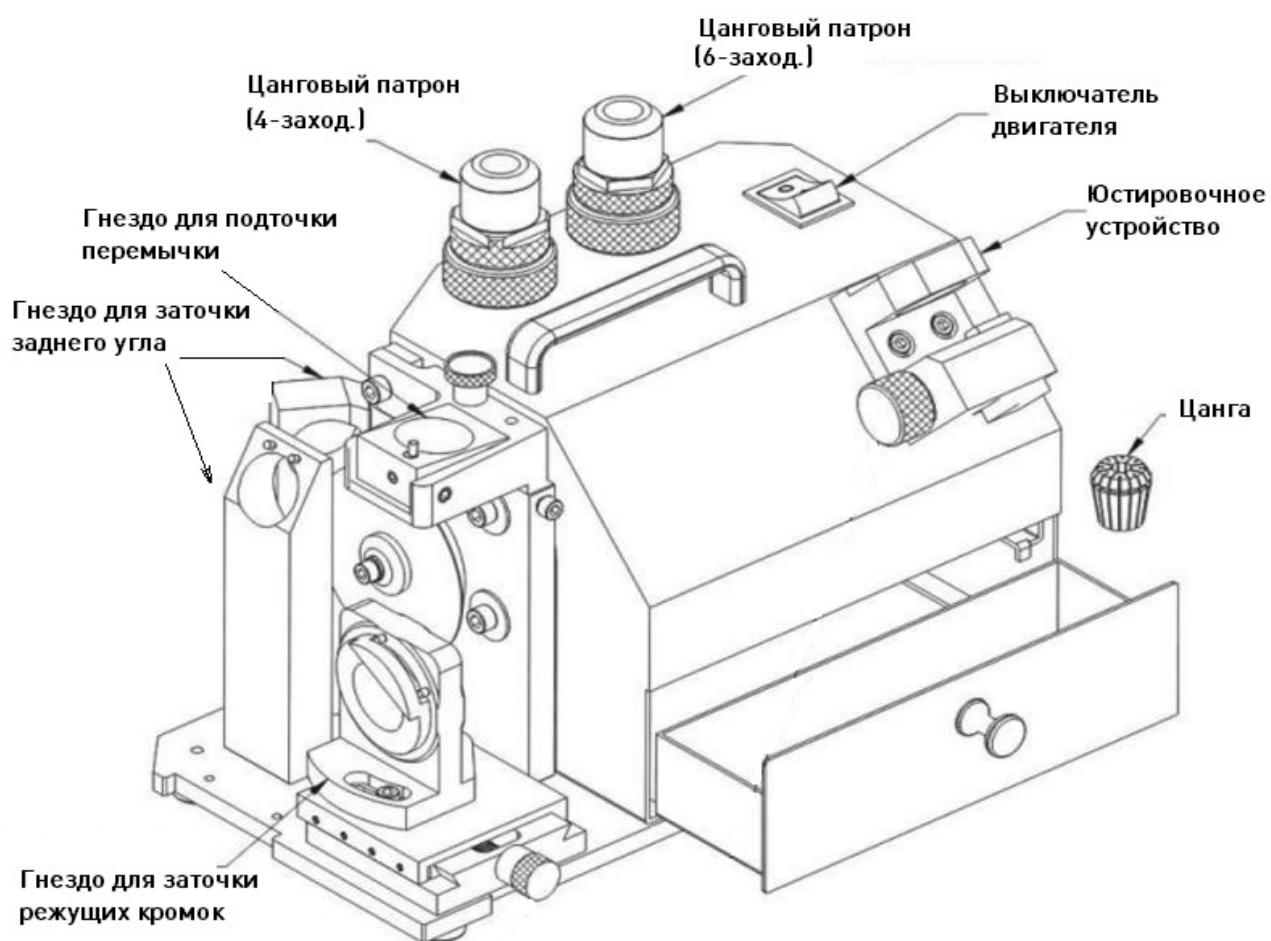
Станок для заточки концевых фрез MR-X3.
